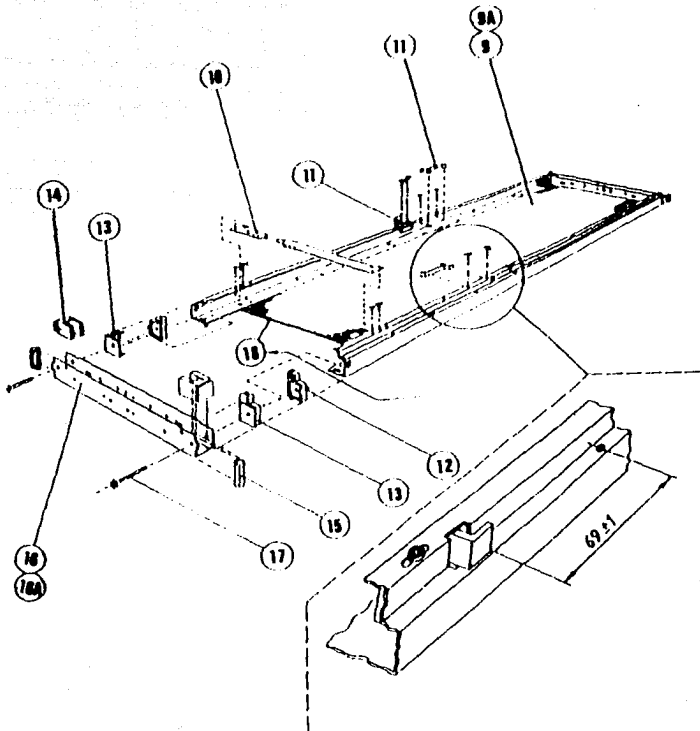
Dibujo representativo del Ensamble de la Tapa.
